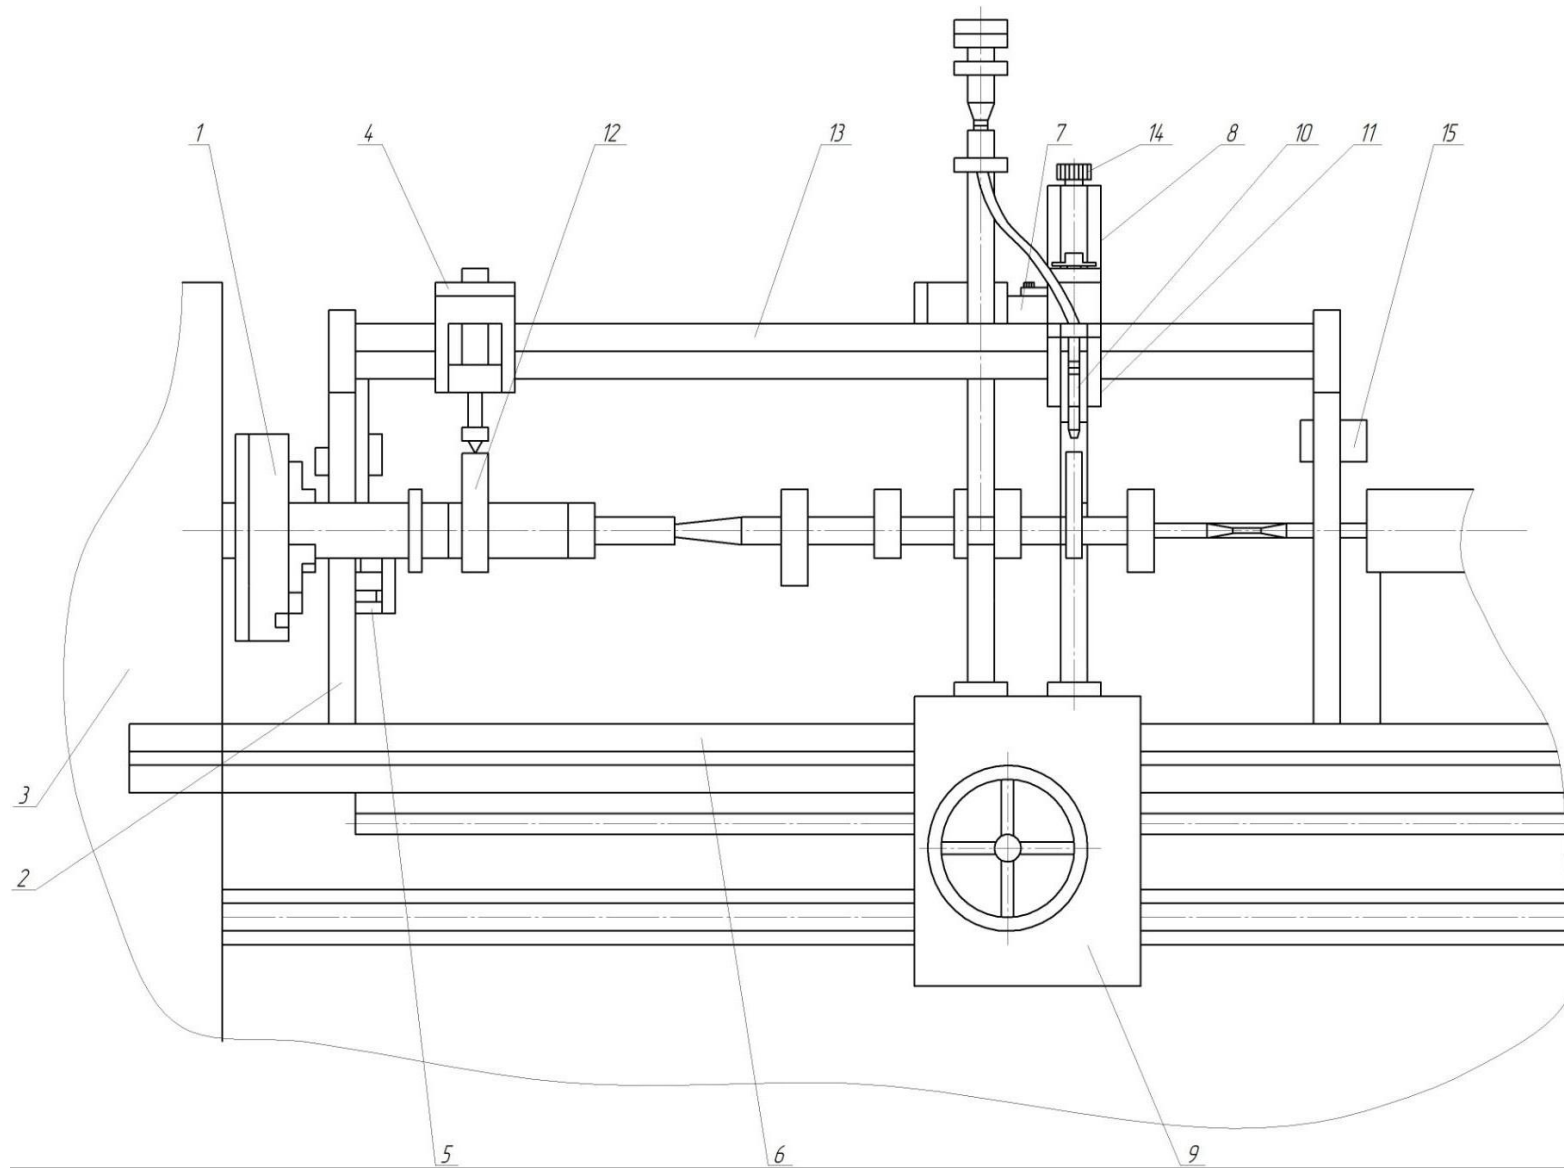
Зальний вигляд установки для плазмового наплавлення розподільчих валів
